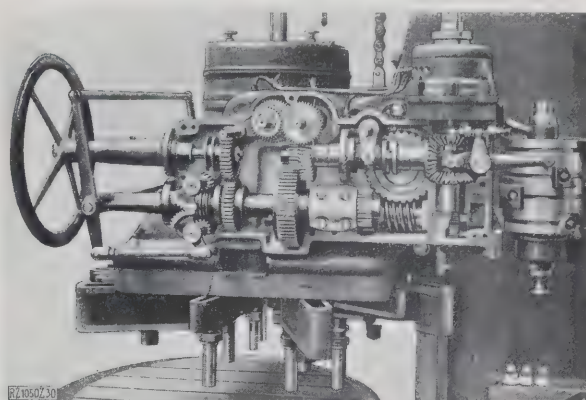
Vorschubräderkasten der Bohrmaschine, Abb. 28. Rechts Trommel mit Anschlägen zum Schalten des Eil- und Bohrvorschubes und des Rücklaufes.
